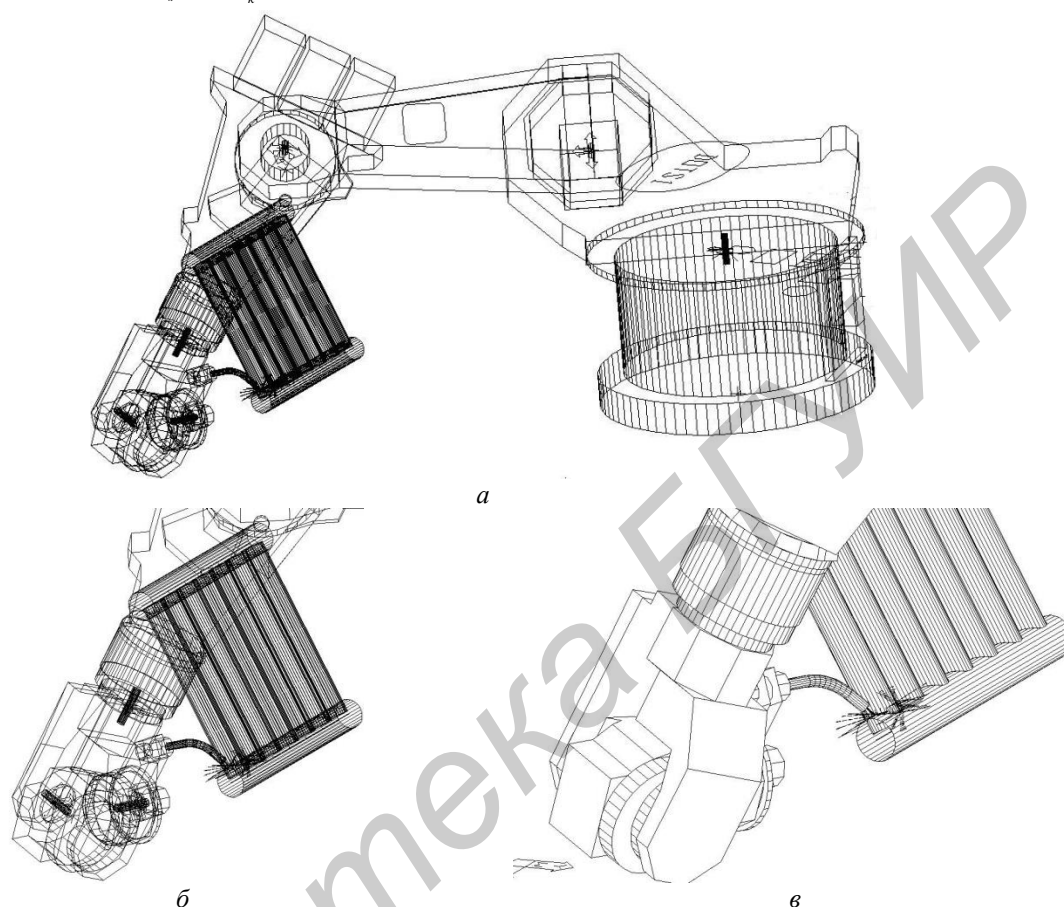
Роботизированная ячейка для дуговой сварки и траектории движения сварочной горелки
